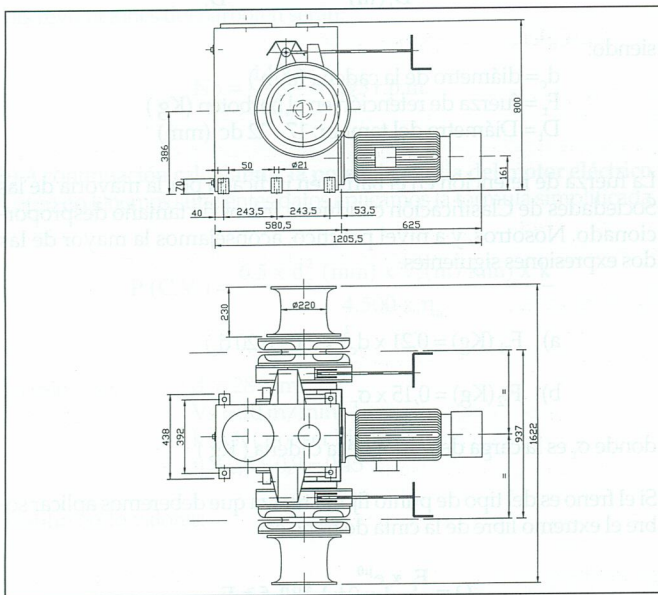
Molinete biancla del tipo horizontal para cadena de 22mm. y accionamiento eléctrico.
